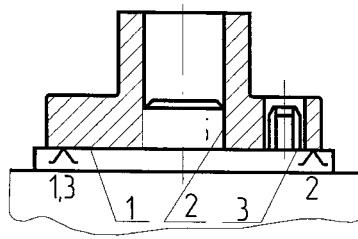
Базирование корпусной заготовки на плоскость, короткую выточку и отверстие
